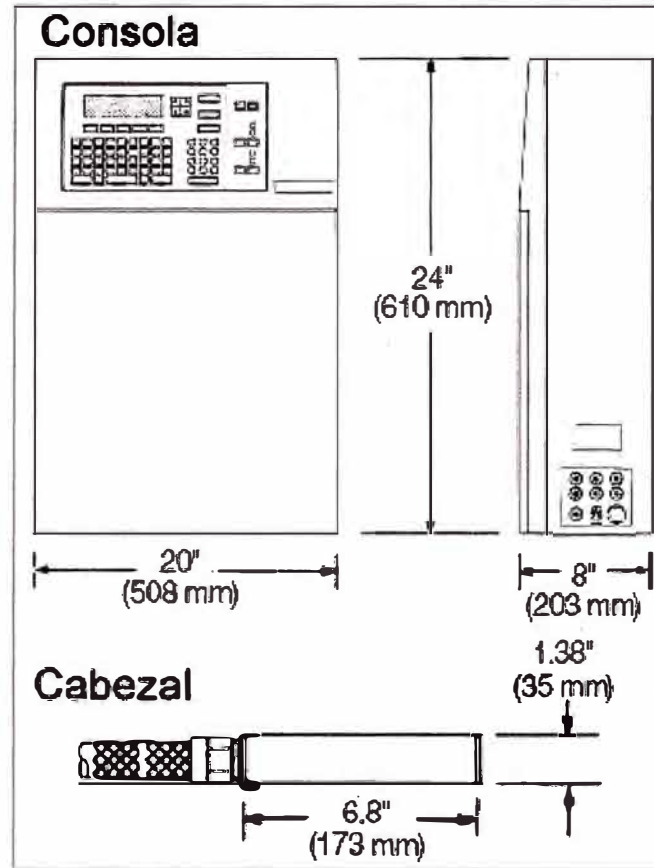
Dimensiones de consola y cabezal (printhead)
